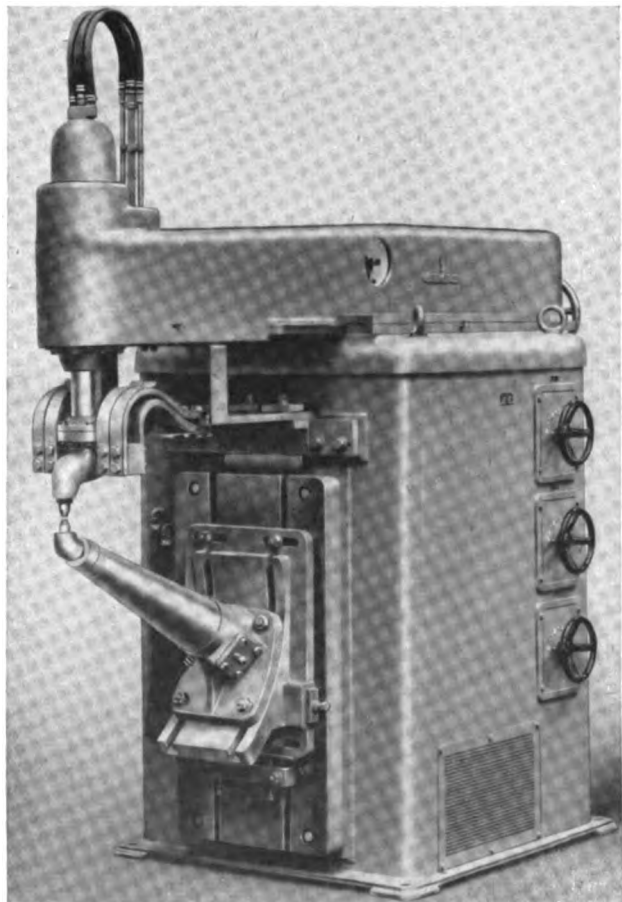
Leichtmetall-Schweißmaschine WP 72
